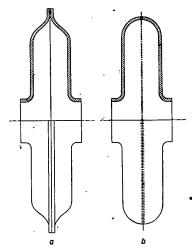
Geschweißte Glieder für Stahlblechradiatoren a widerstandgeschweißt, b autogen geschweißt
